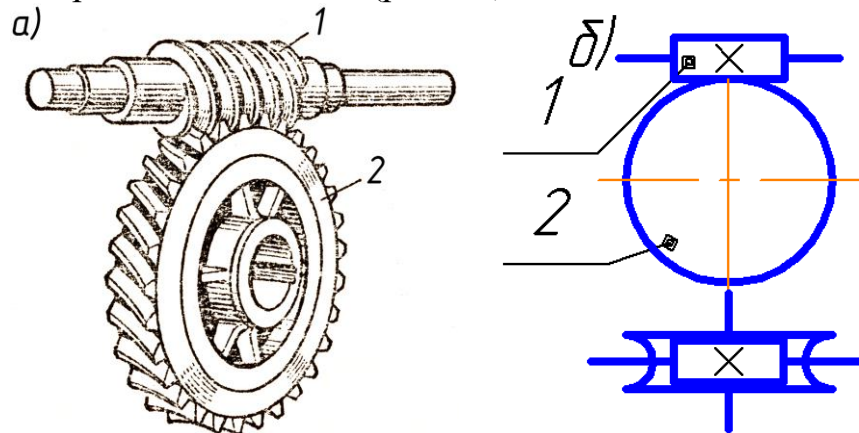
Червячная передача: а) общий вид; б) кинематическая схема
